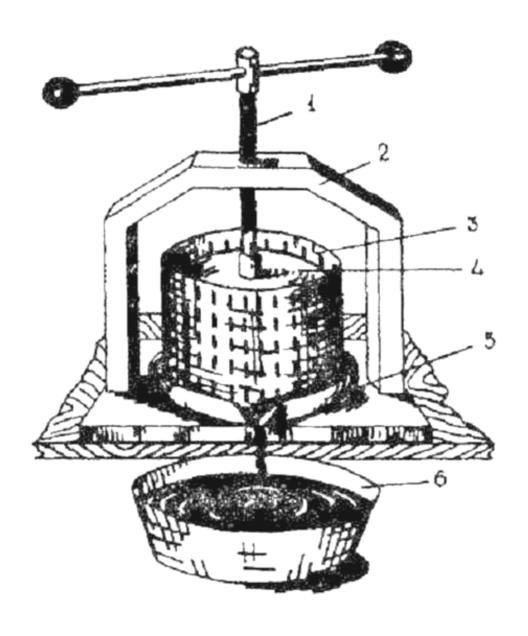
Винтовой пресс: 1 - винт; 2 - станина пресса; 3- сетчатая корзина; 4 - прижимной диск; 5 - противень; 6 - емкость для сока.
